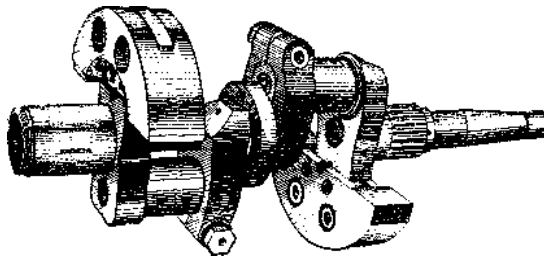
Двухколенный коленчатый вал двухрядного звездообразного двигателя
